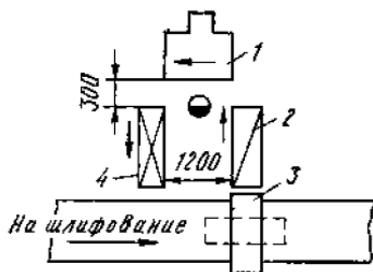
Схема организации рабочего места у сверлильно-пазовального станка СВА-2:
